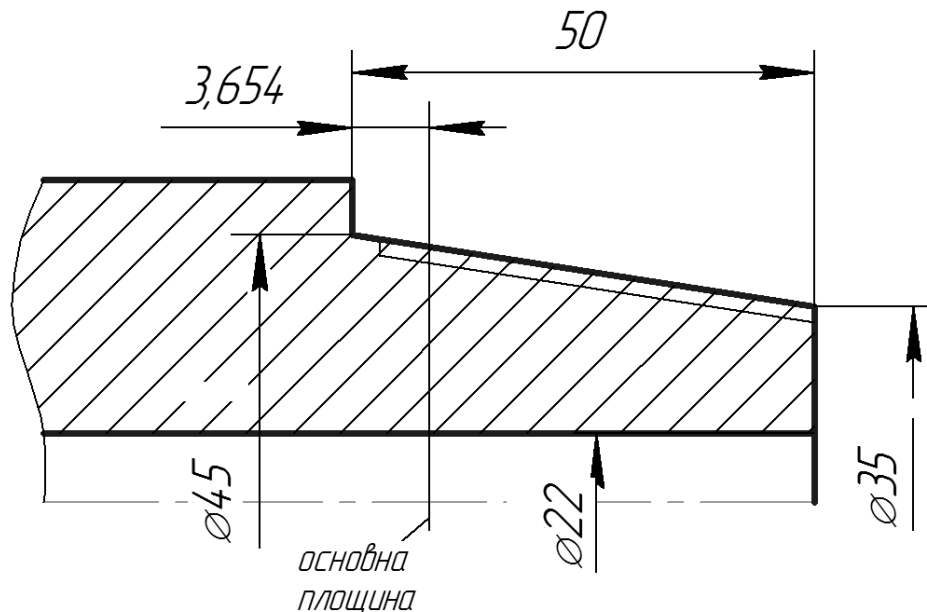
Схема ніпеля замкового різьбового з'єднання 3-42
